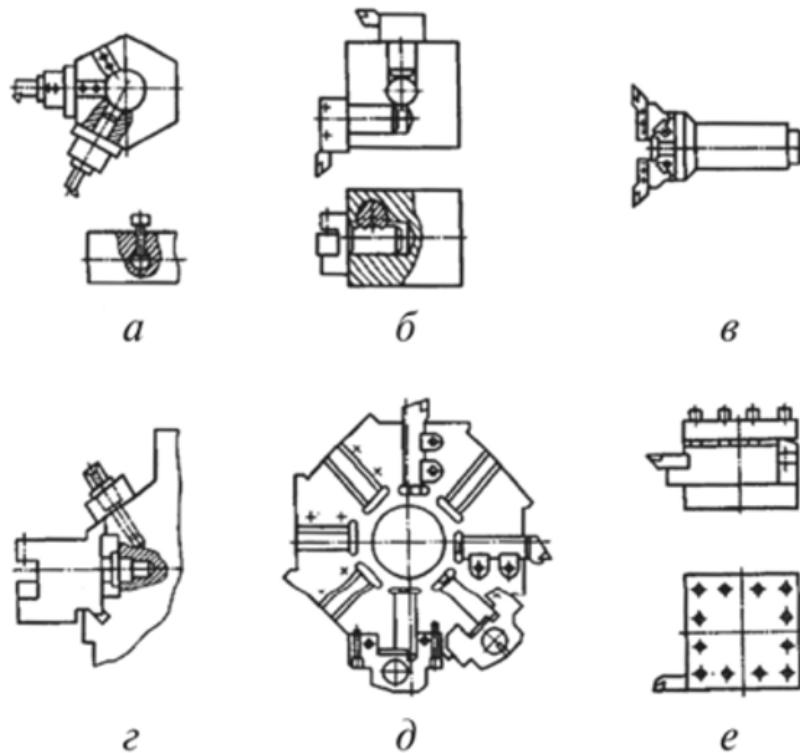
Схеми варіантів кріплення на токарних верстатах з ЧПУ
